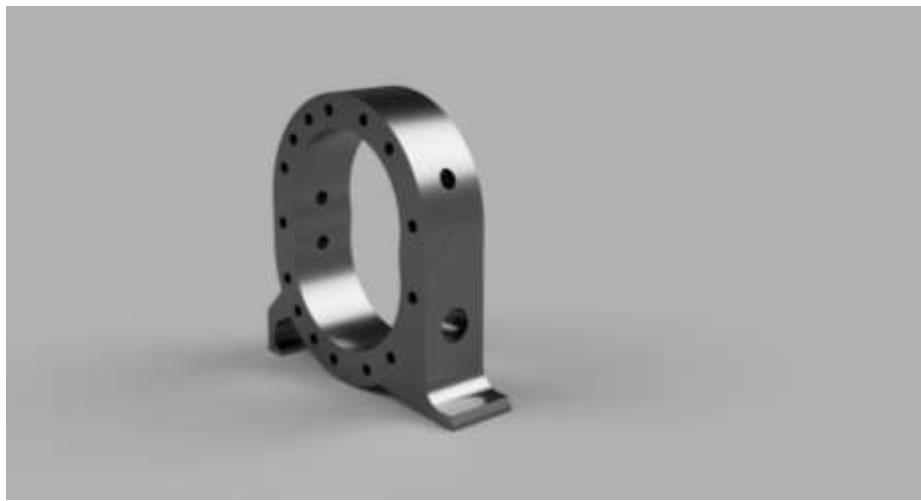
Деталь „ Корпус двигуна Ванкеля”
